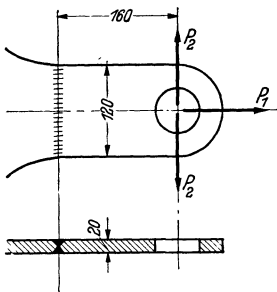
Lagerblech-Anschluß durch Stumpfnah.
